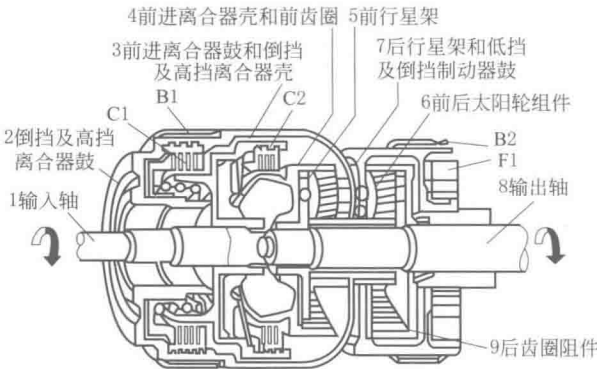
辛普森式 3 挡行星齿轮变速器
